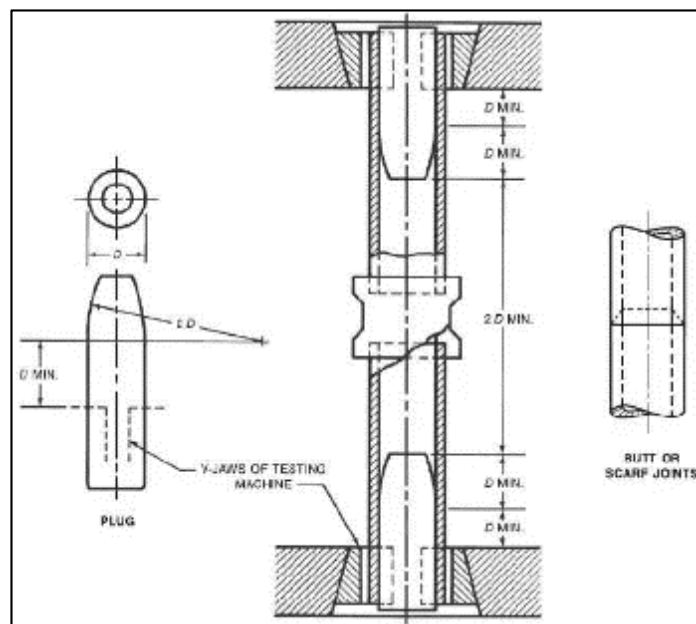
Probetas para el ensayo de tracción de tuberías de diámetro pequeño para juntas de traslape y a tope.
